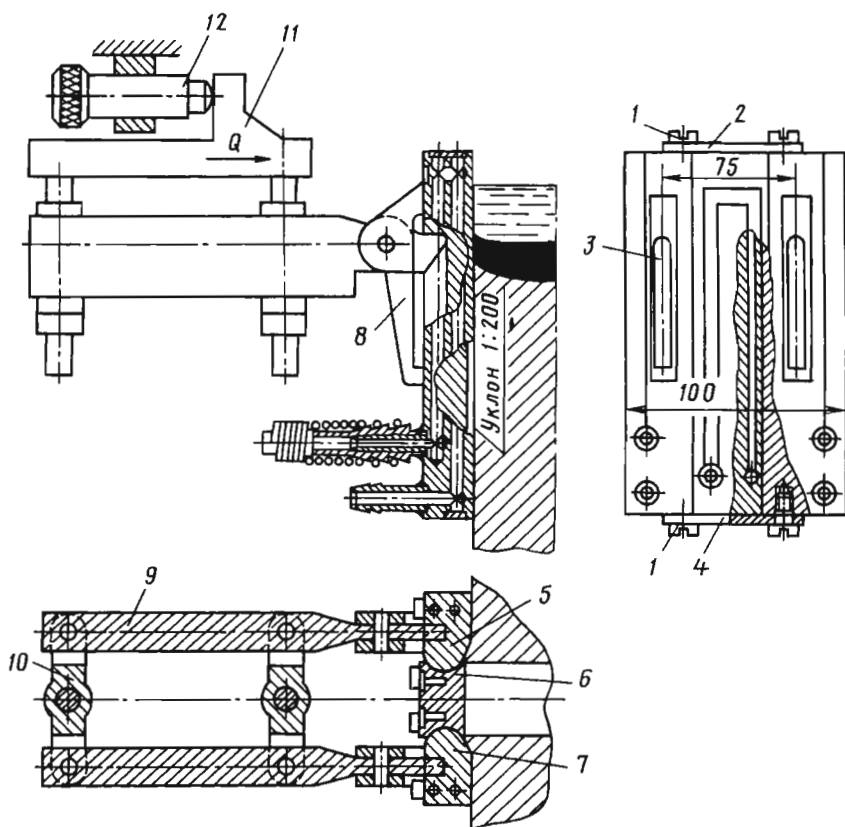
Конструкция шарнирного ползуна с балансирующей подвеской:
